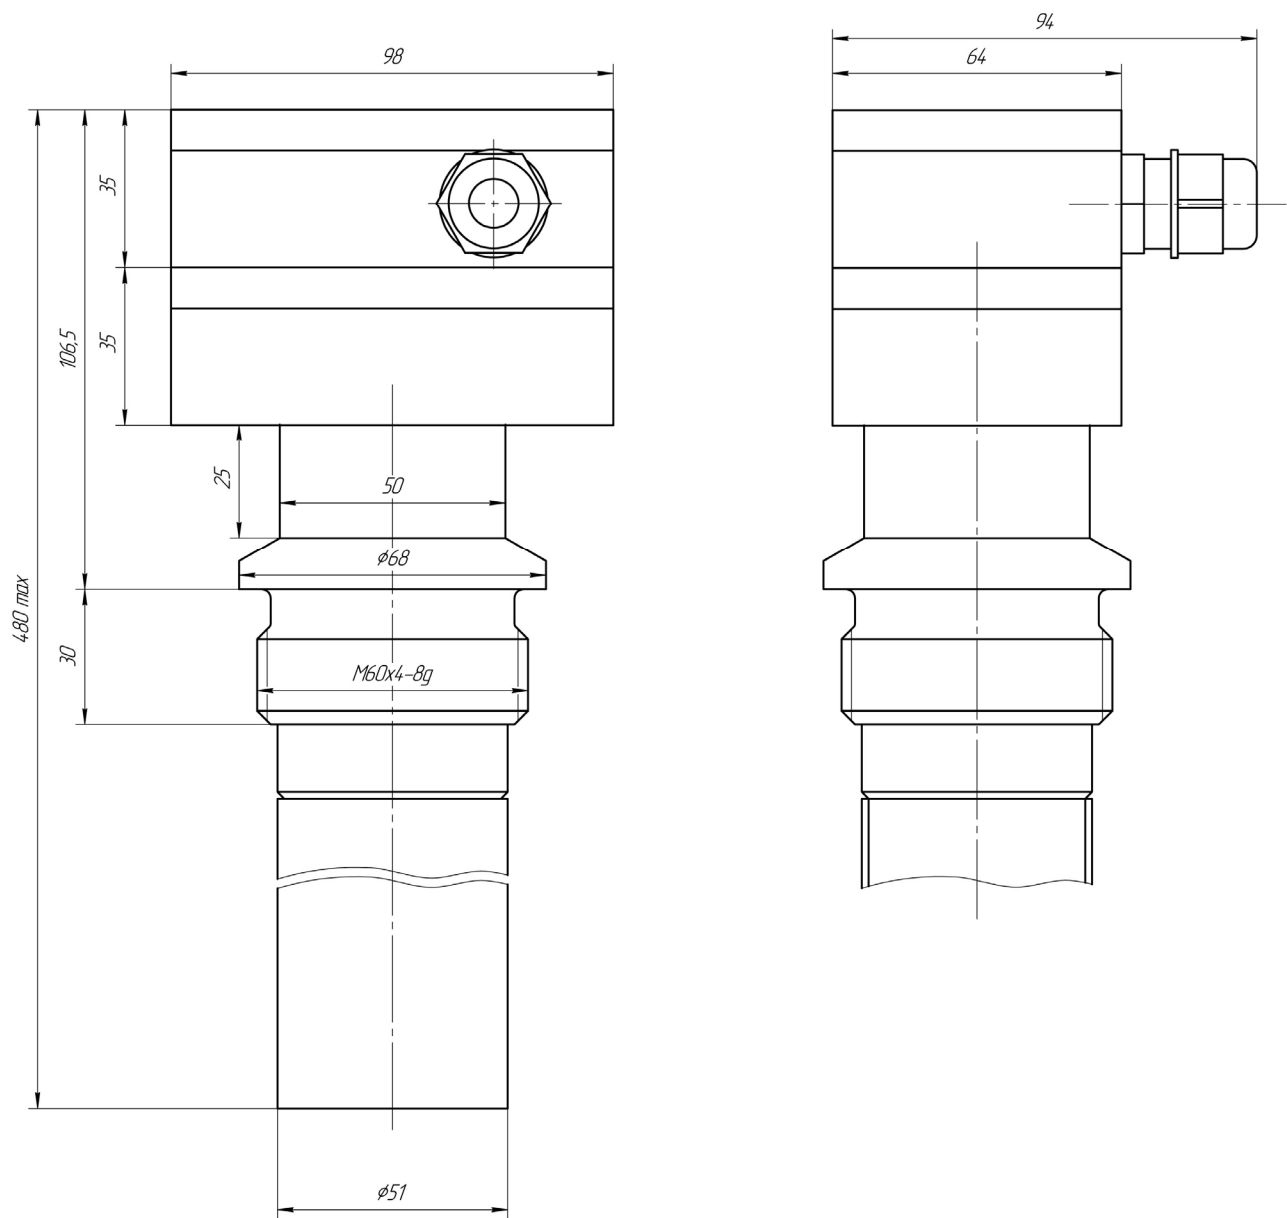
Габаритный чертеж первичного преобразователя ДЖС-7В
